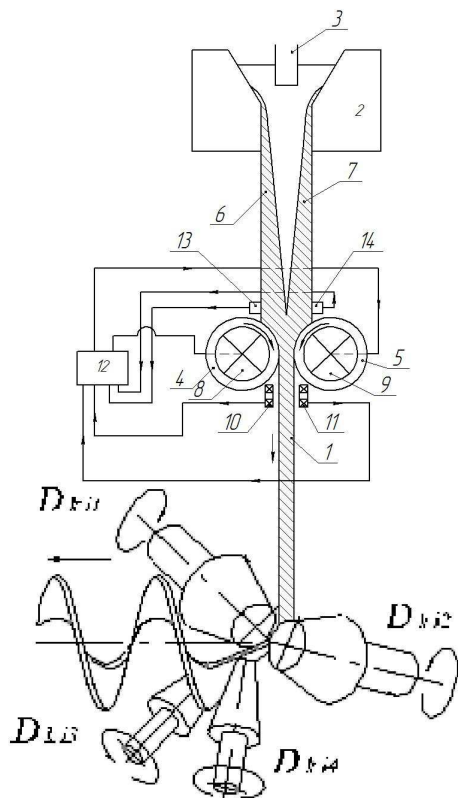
Конструкція для безперервного лиття гвинтових заготовок
